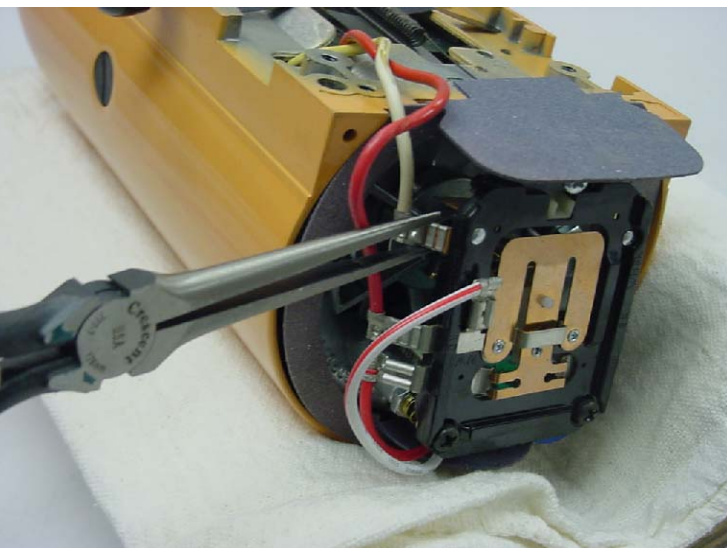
Flachsteckkontakte des Motorstators von der Steuerplatte abziehen.
